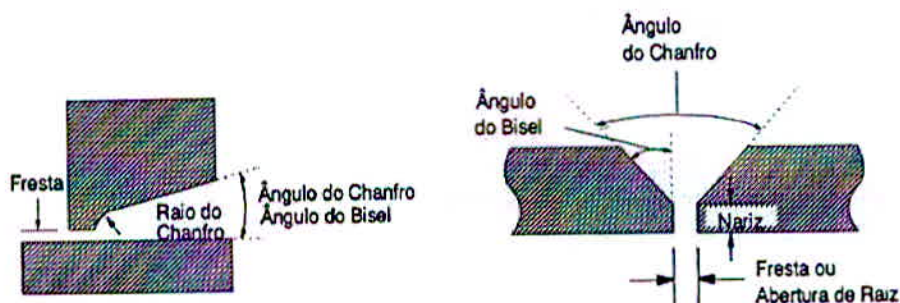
Características dimensionais de chanfros usados em soldagem.
